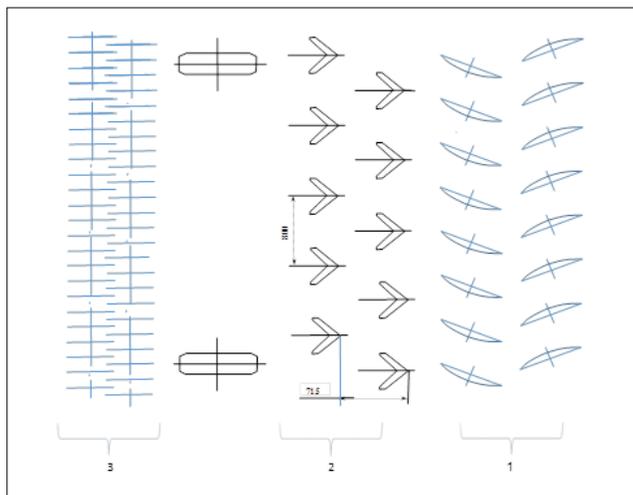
Схема расстановки рабочих органов на рыхлителе-выравнивателе РВК-4 (вид сверху): 1 – два ряда сферических дисков; 2 – два ряда стрелчатых лап; 3 – двухвалный игольчато-дисковый каток
